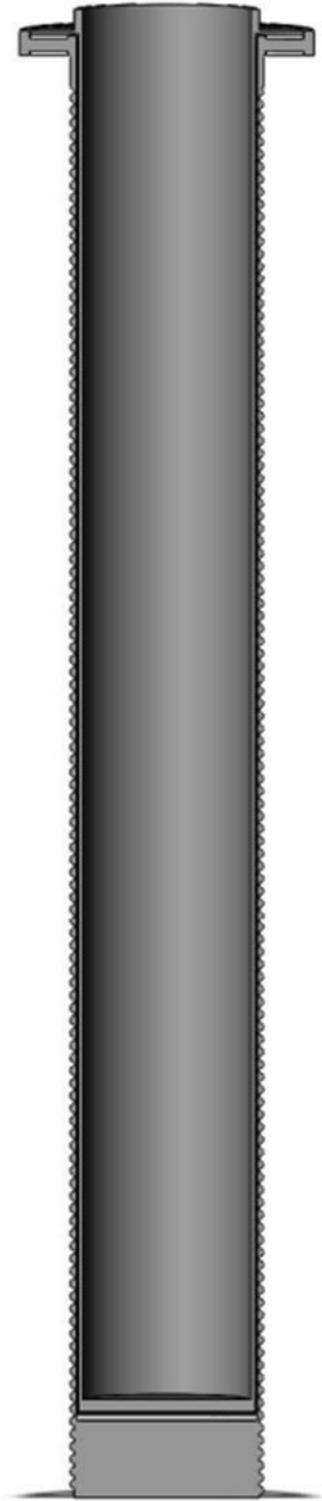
Корпус магнито-реологического демпфера с композитным вкладышем
